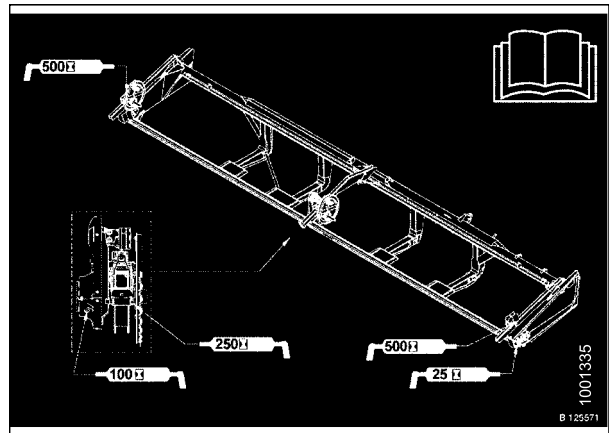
Наклейка с основными точками смазки на жатке с одинарным ножом
